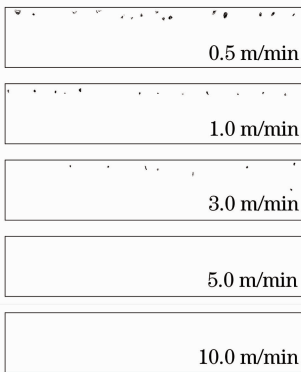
不同焊接速度条件下焊缝气孔X射线图
